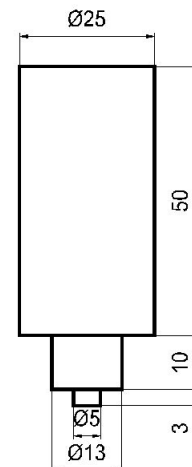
Dimensiones de la herramienta de soldadura (mm).
